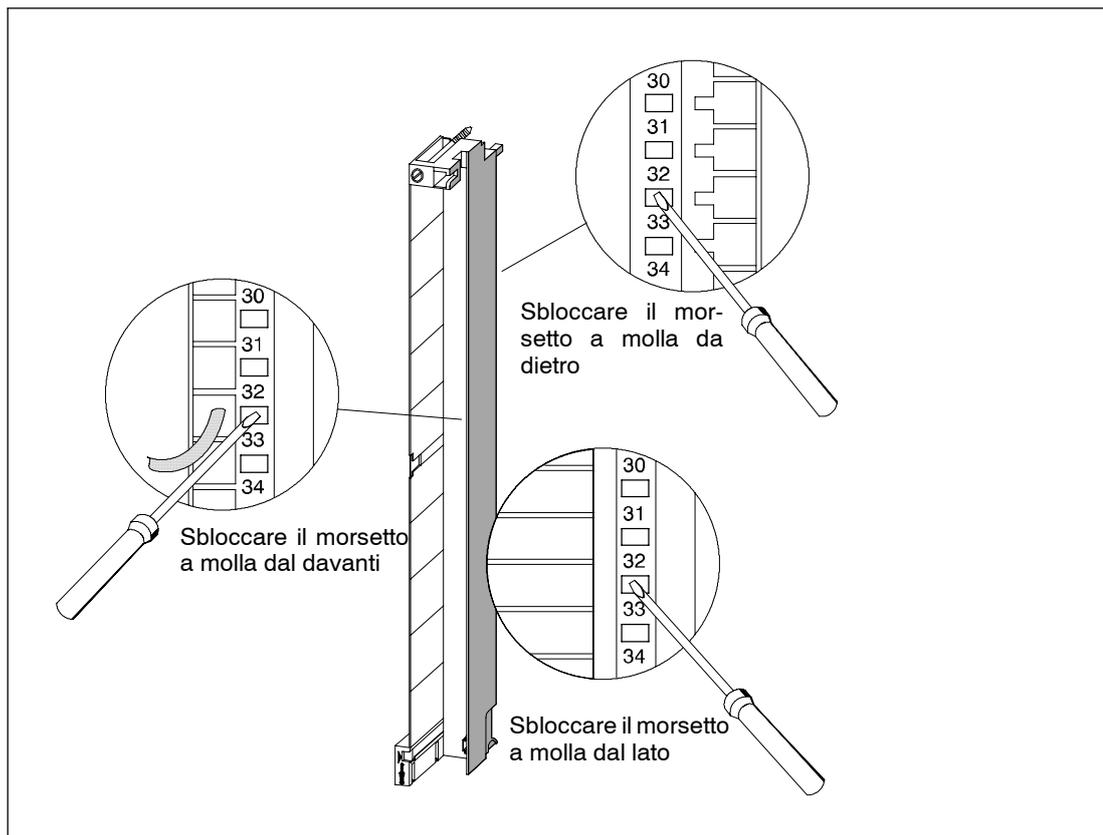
Cablaggio del connettore frontale, tecnica a molla
